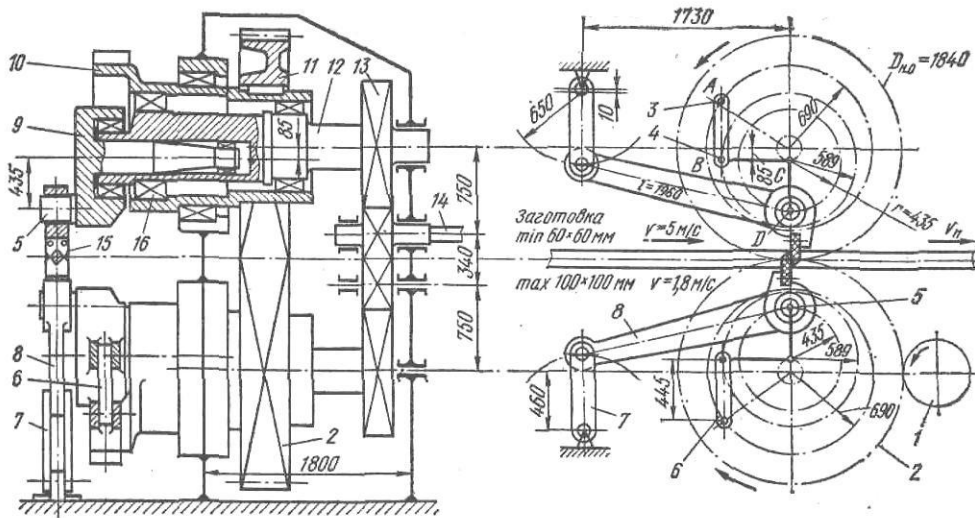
Конструктивно-кинематическая схема кривошипно-шатунных летучих ножей с эксцентриковым механизмом пропуска реза для резки горячей заготовки
